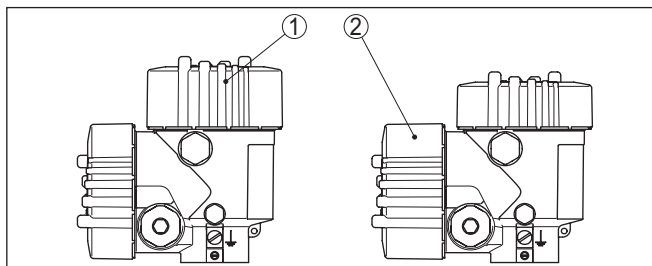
Установка модуля индикации и настройки в двухкамерном корпусе
